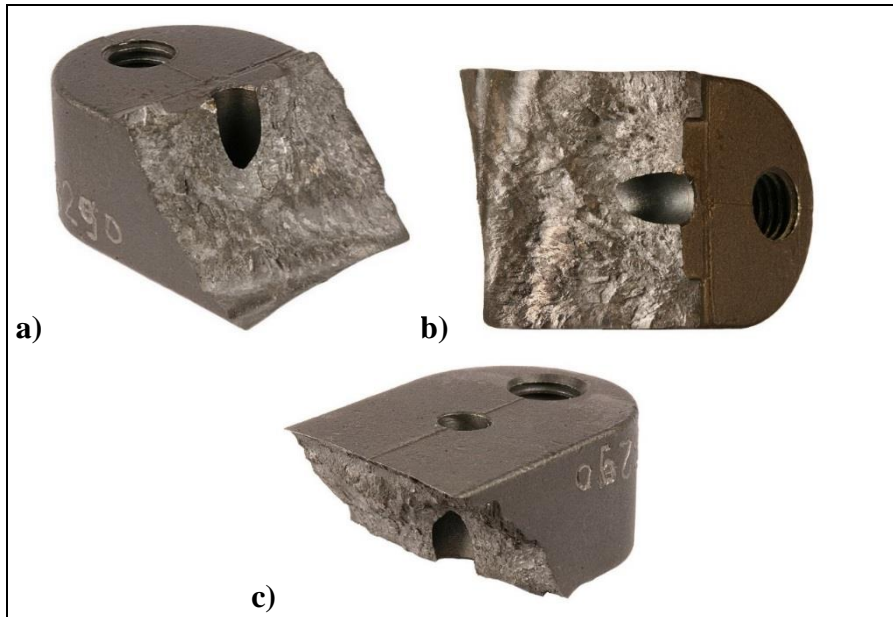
Pieza B. Diferentes vistas de su superficie de fractura.
